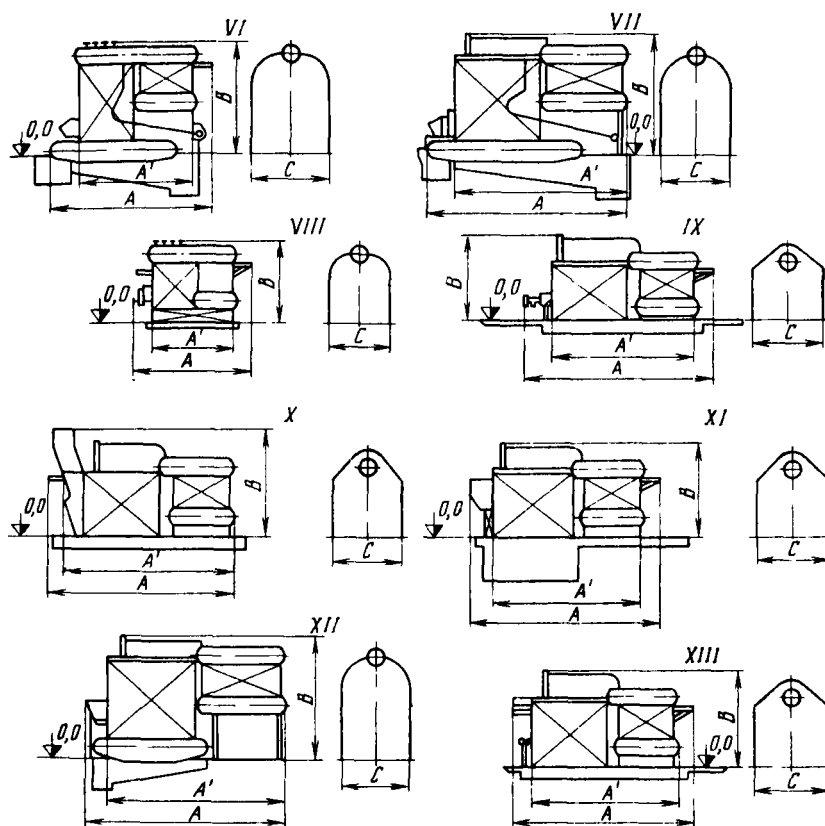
Схемы компоновок котлов типа ДКВР с различными топочными устройствами и габаритные размеры:
